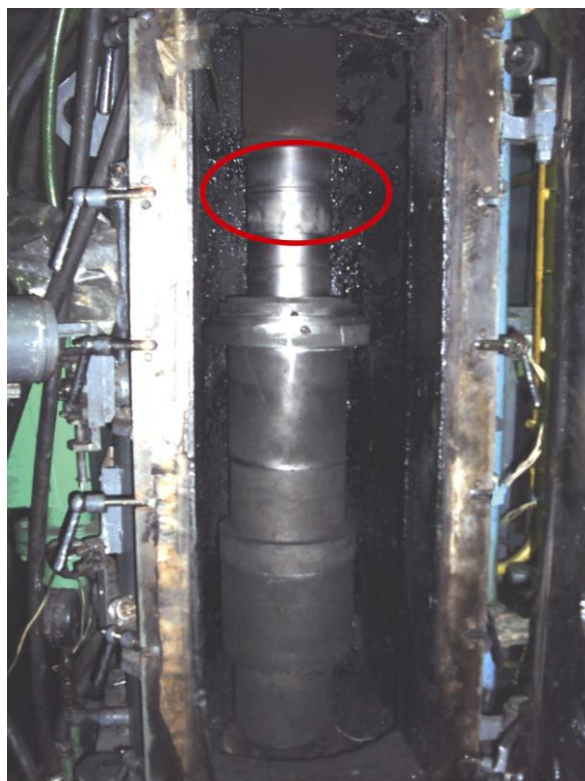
Камера установки АГАТ-1.6 із встановленою заготовкою
